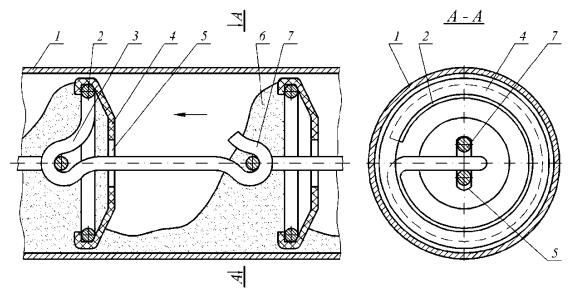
Конструктивна схема робочого органа шайбового конвеєра
